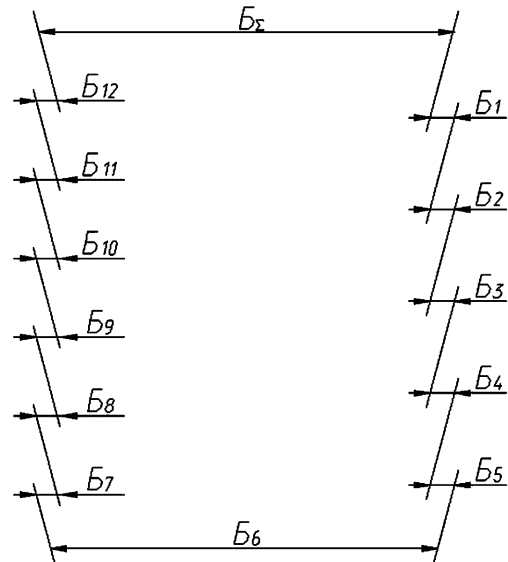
Схема розмірного ланцюга зубчастієї передачі
